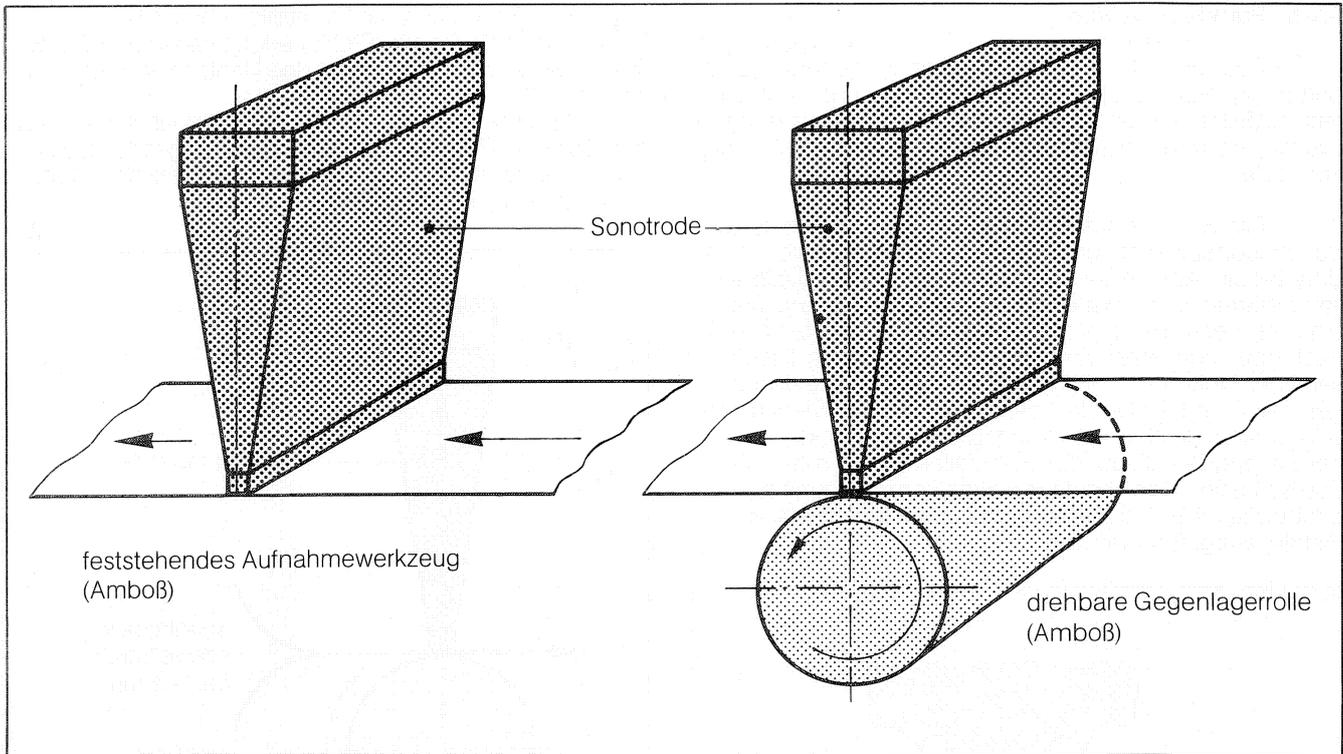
Ultraschall-Nahtschweißen diskontinuierlich durch Strichnahtsonotrode
